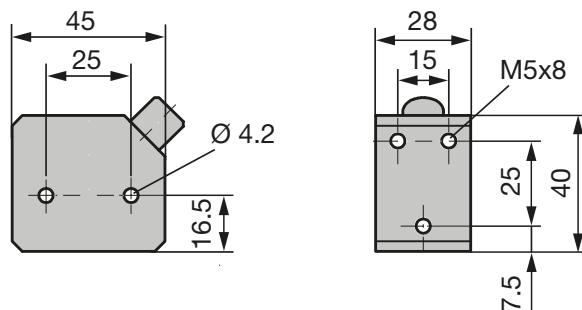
Dimensions de montage du capteur de position BTL5-P-4500-1
